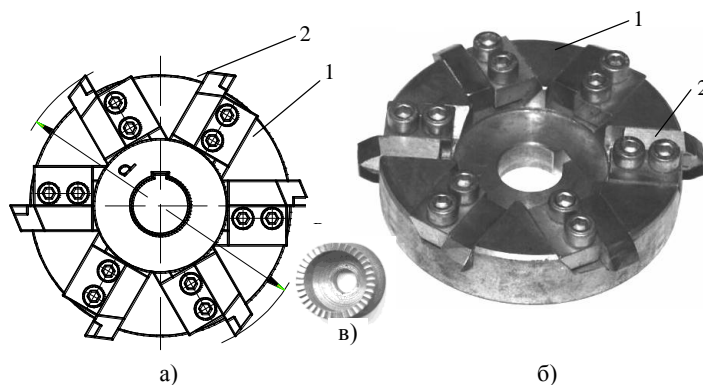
Конструкция резцовой головки (а, б) и деталь (в) с ТЗК:
